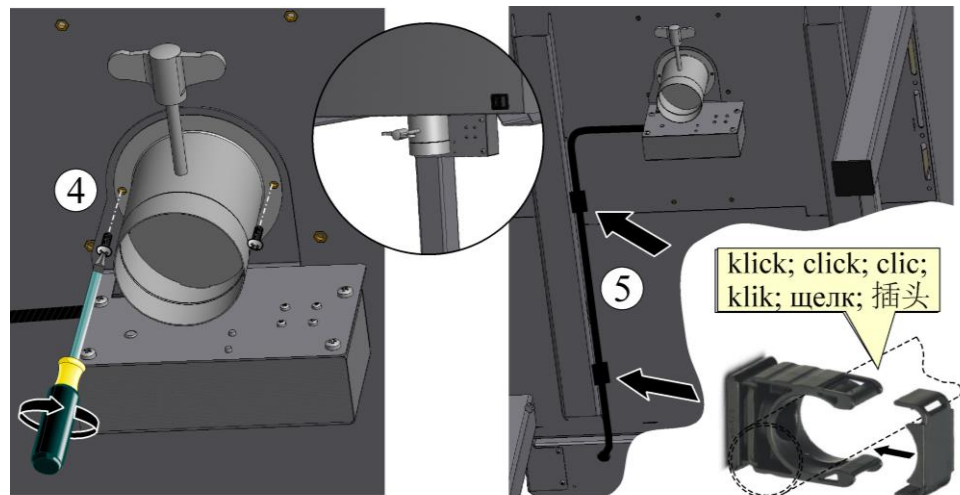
Montagem da tampa do ar de alimentação e instalação do cabo (semelhante à figura)
